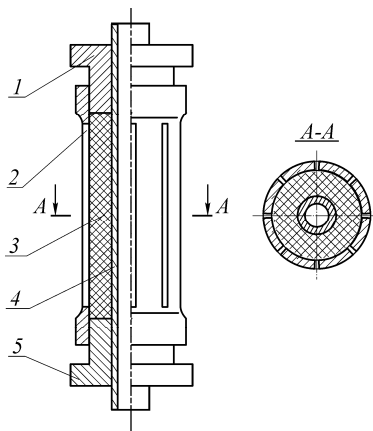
Схема базової конструкції оболонкової пружини (1, 5 – поршні; 2 – несуча оболонка; 3 – деформівний заповнювач, 4 – ствол)
